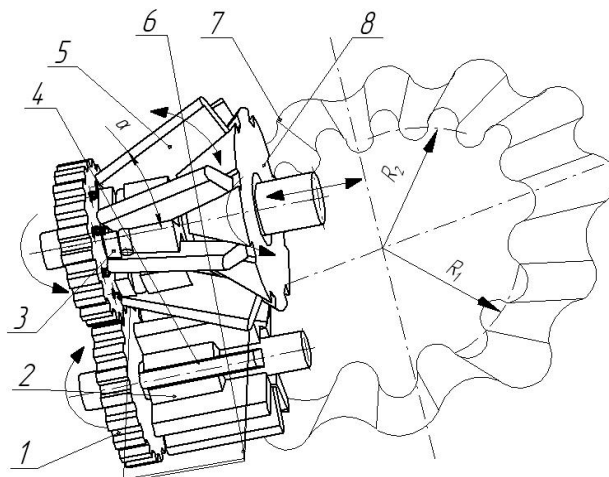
Схема інструменту для виготовлення гвинтових гофрованих заготовок із змінним радіусом
